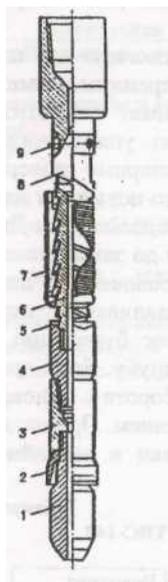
Труболовка внутренняя спиральная РГВС-14Ф: 1-наконечник;2-уплотнение манжетное; 3,4-персводники; 5-кольцо расцепное, 6-хор-лус; 7-втулка захватная; 8-втулка управляющая; 9-винт спиральный
